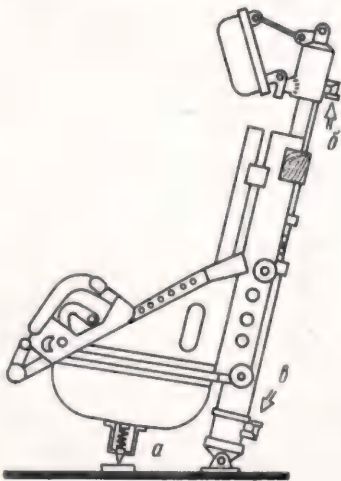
а — блокирующий микровыключатель; б и в — подвод воздуха.
